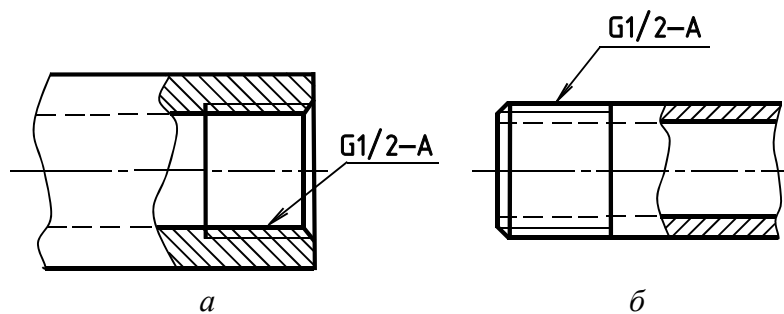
Обозначение на чертеже трубной резьбы:
